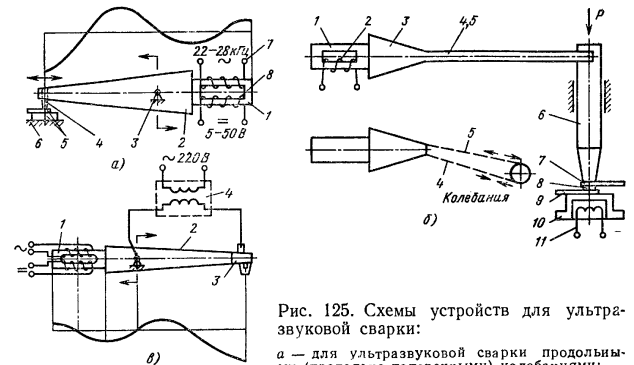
Схемы устройств для ультразвуковой сварки:
